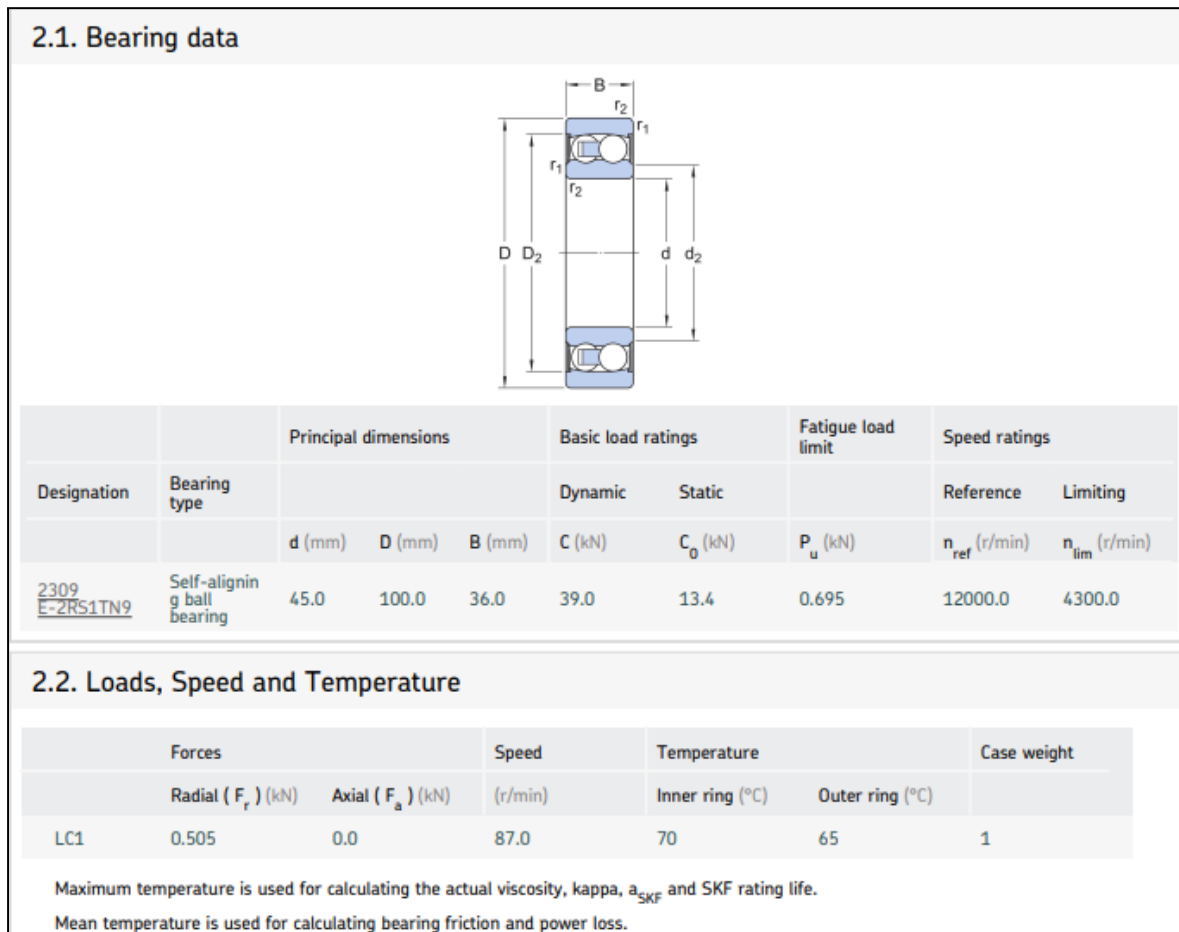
Características de rodamiento de bolas seleccionado para el lado izquierdo del tornillo sin fin. *Realización propia.
